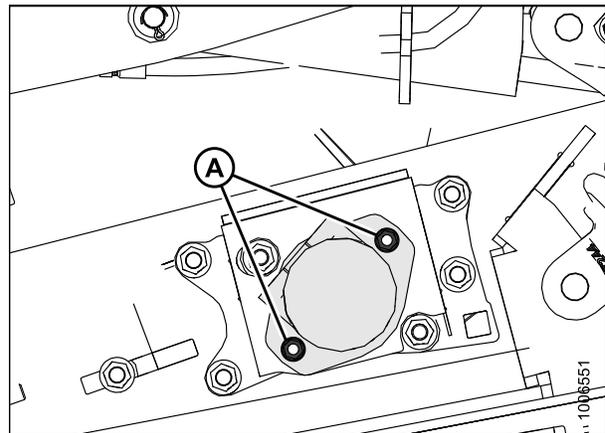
Motor hidráulico delantero; lado izquierdo
